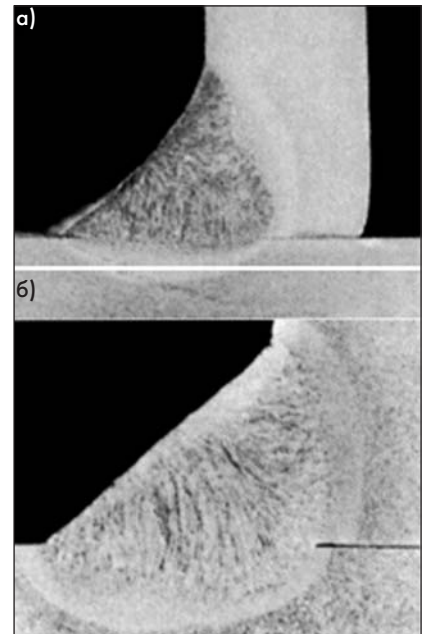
Формы проплавления при сварке сплошной проволокой диаметром 1,0 мм в смеси газов (а) и порошковой рутиловой проволокой E71T-1 в защитном газе CO_2 (б)
